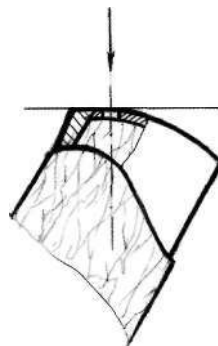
Направление сверления отверстия под гайку для винта, крепящего навершие
